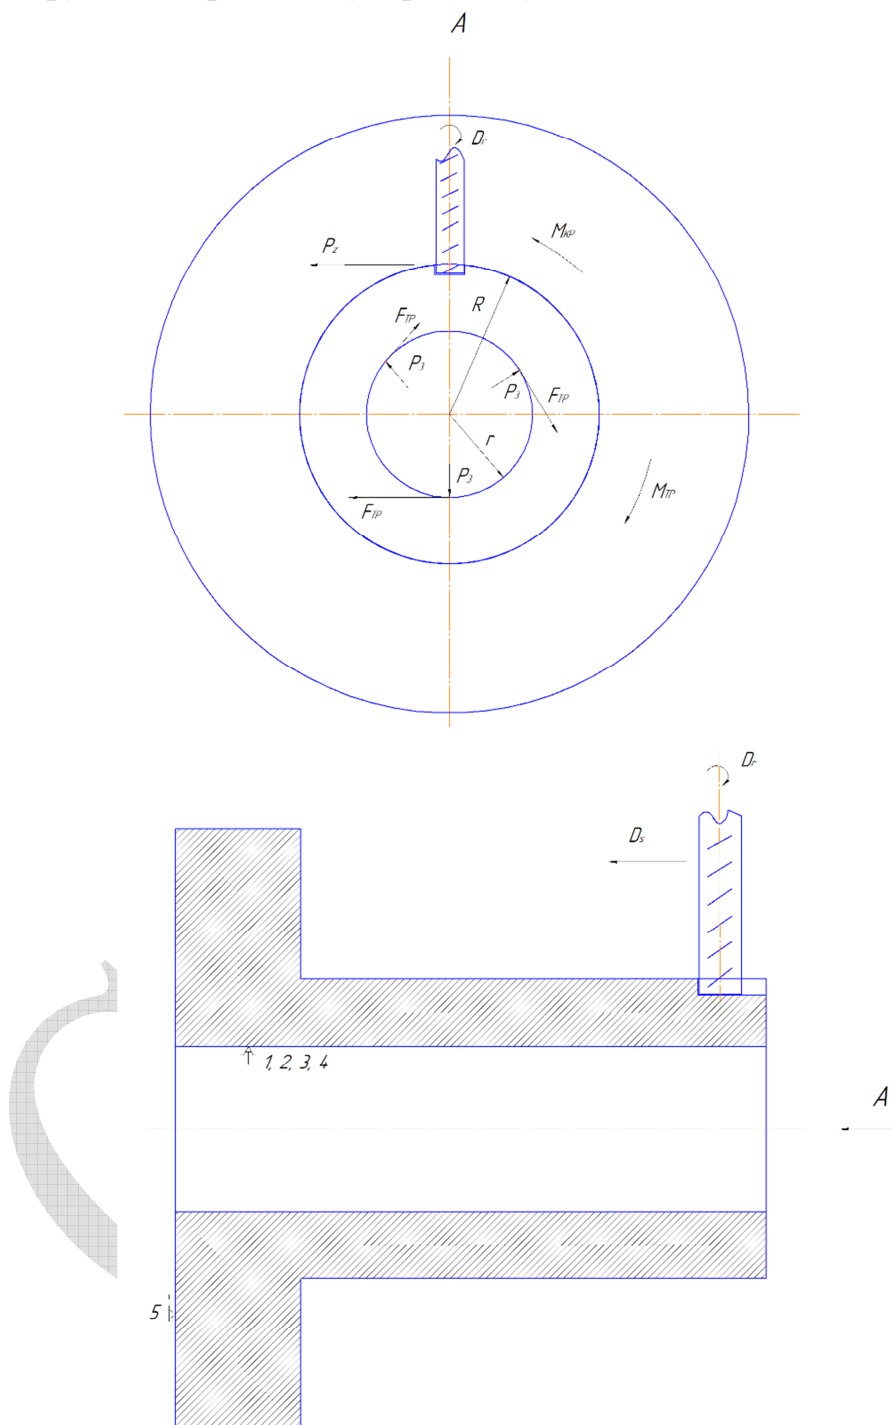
Схема розрахунку сили закріплення заготовки.
